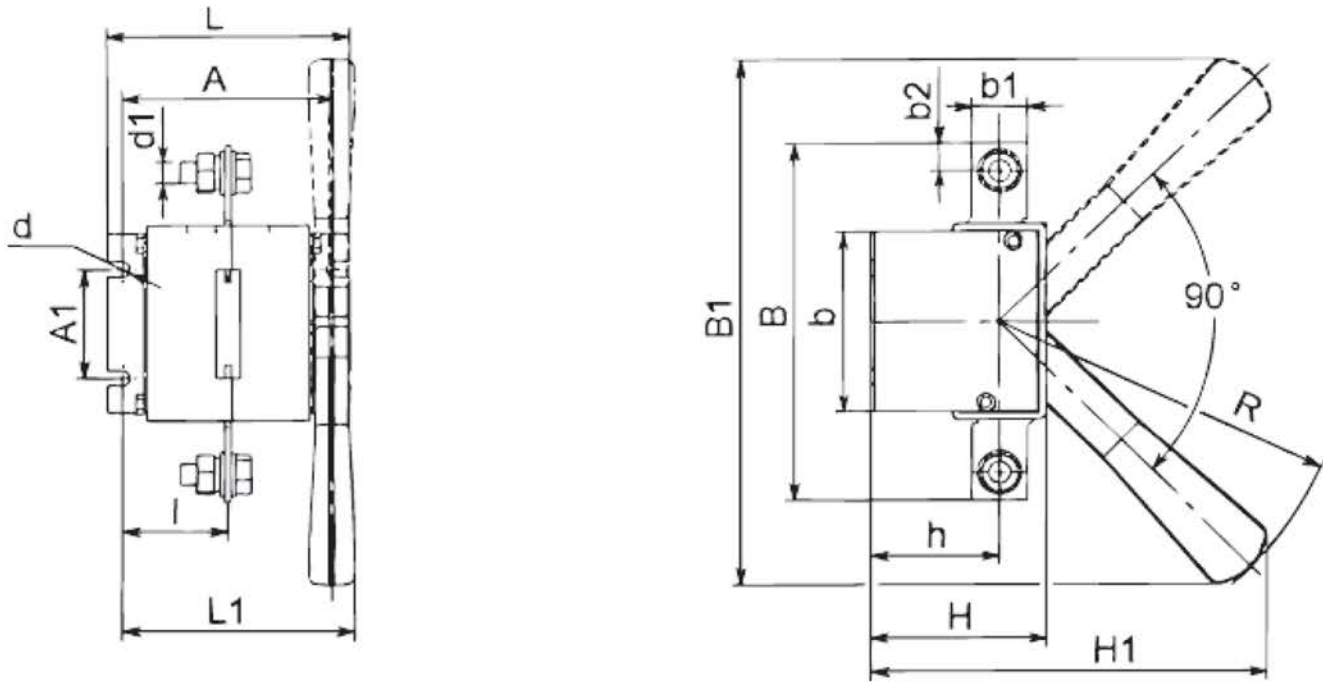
Выключатель-разъединитель однополюсный на два направления с боковой рукояткой.
